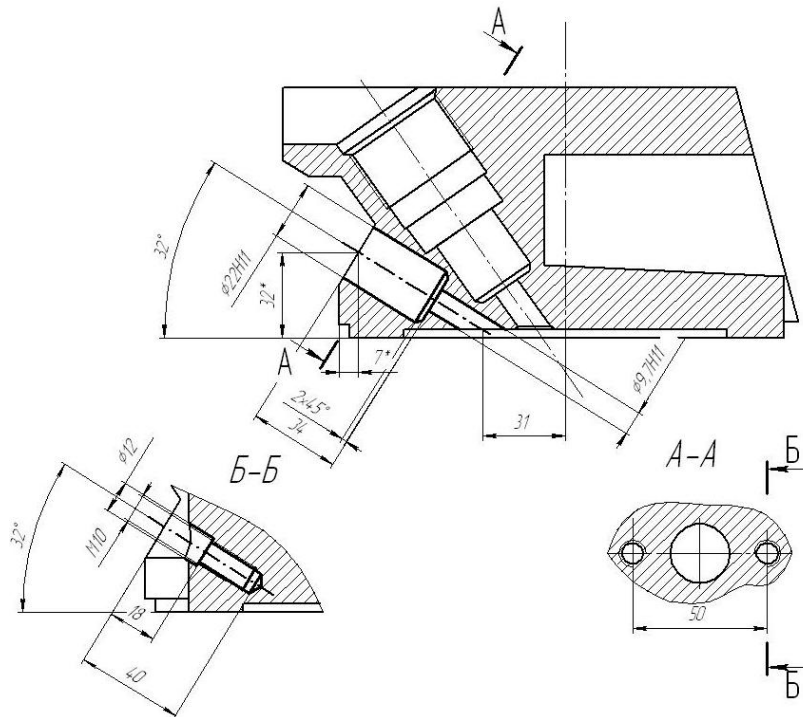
Рабочий чертеж отверстия в головке цилиндра дизеля 2Ч10,5/12,0, выполненного для установки штифтовой форсунки
